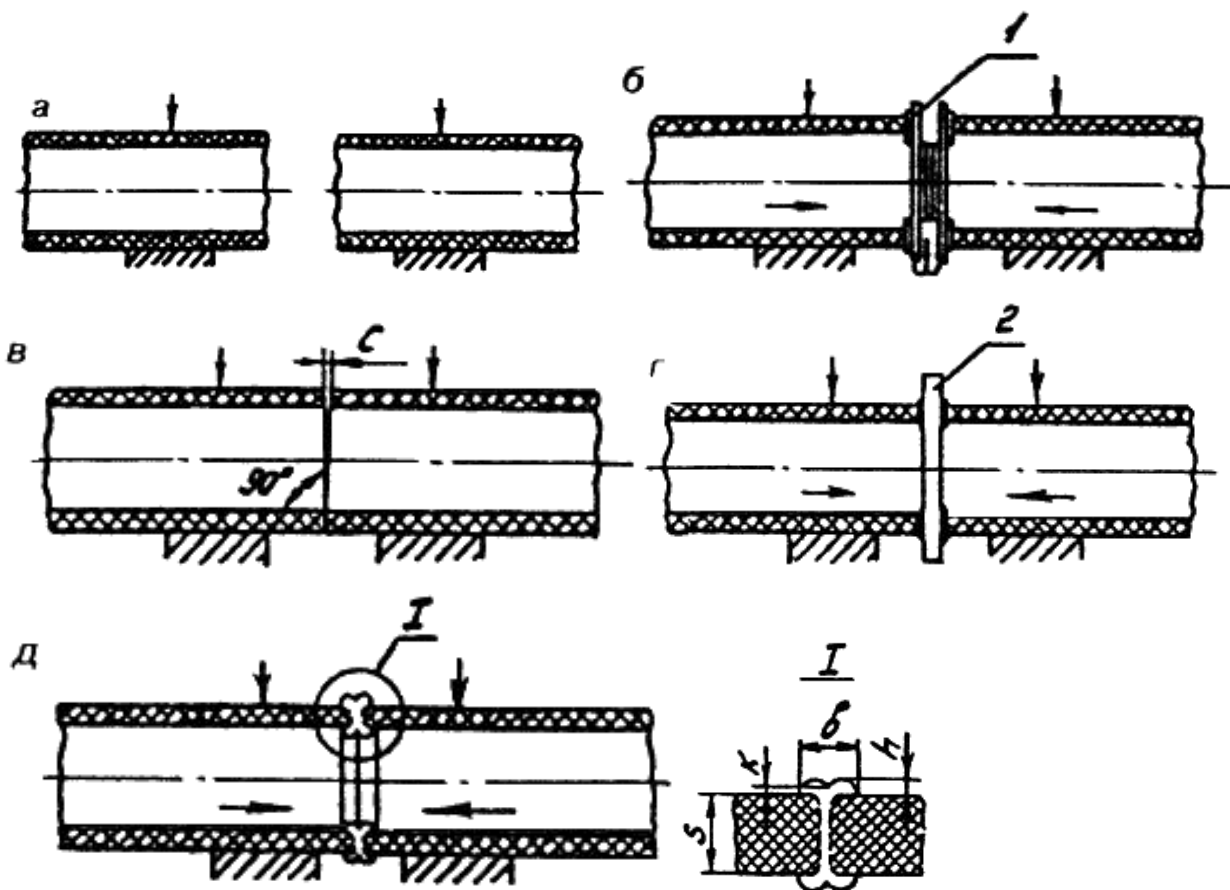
Последовательность сварки труб нагретым инструментом: центровка и закрепление в зажимах сварочной машины концов свариваемых труб (а); механическая обработка торцов труб с помощью торцовки (б); проверка точности совпадения торцов по величине зазора (в); нагрев и оплавление свариваемых поверхностей нагретым инструментом (г); осадка стыка (д)
